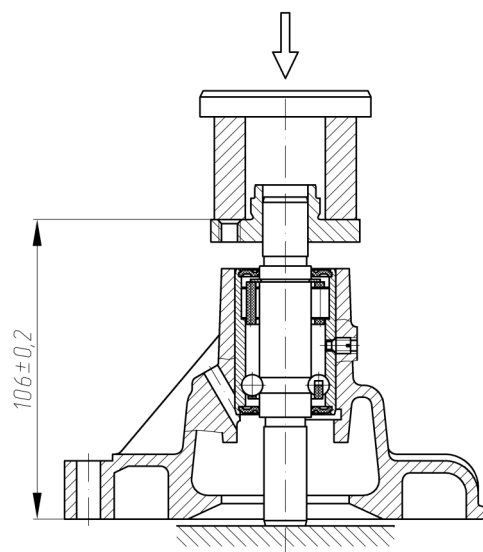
Напрессовка ступицы шкива водяного насоса
